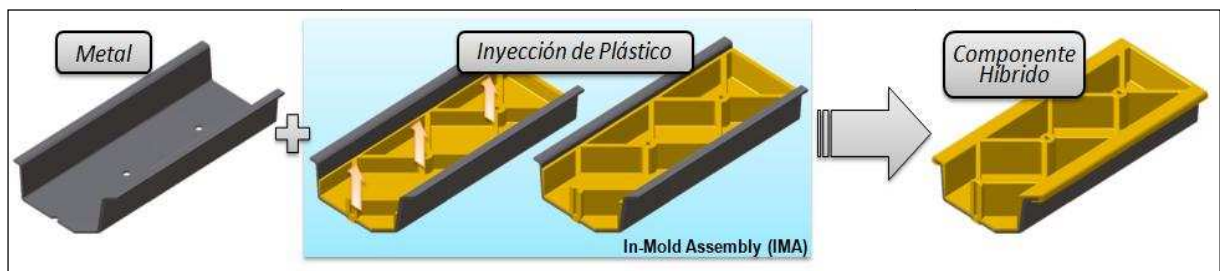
PROCESO PRODUCTIVO DE UNIÓN IN-MOLD ASSEMBLY. IMA
